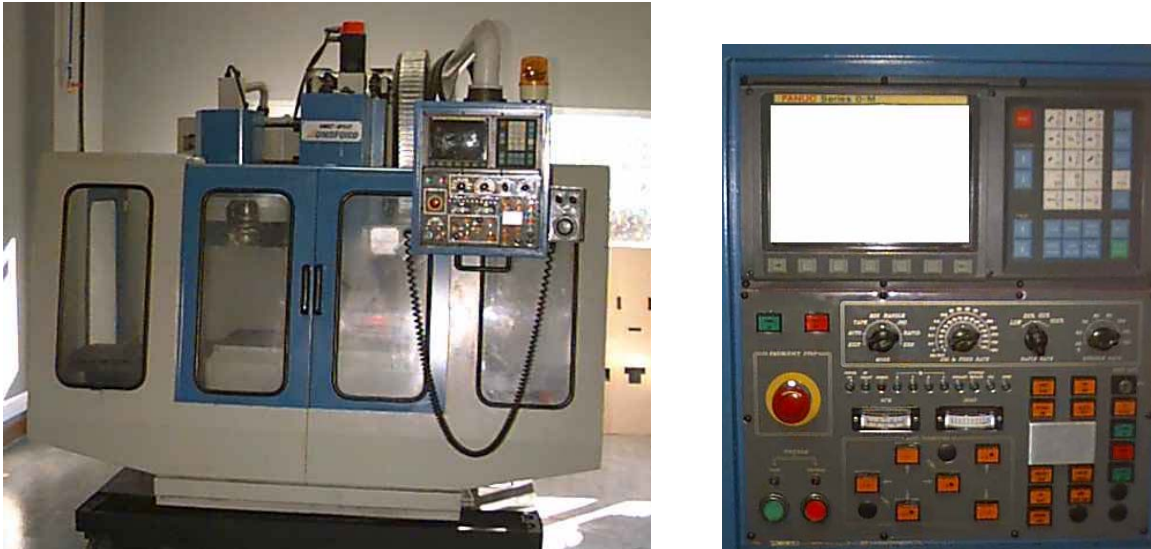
Centro de mecanizado FANUC. Máquina-herramienta fresadora y su panel de control (CNC).
